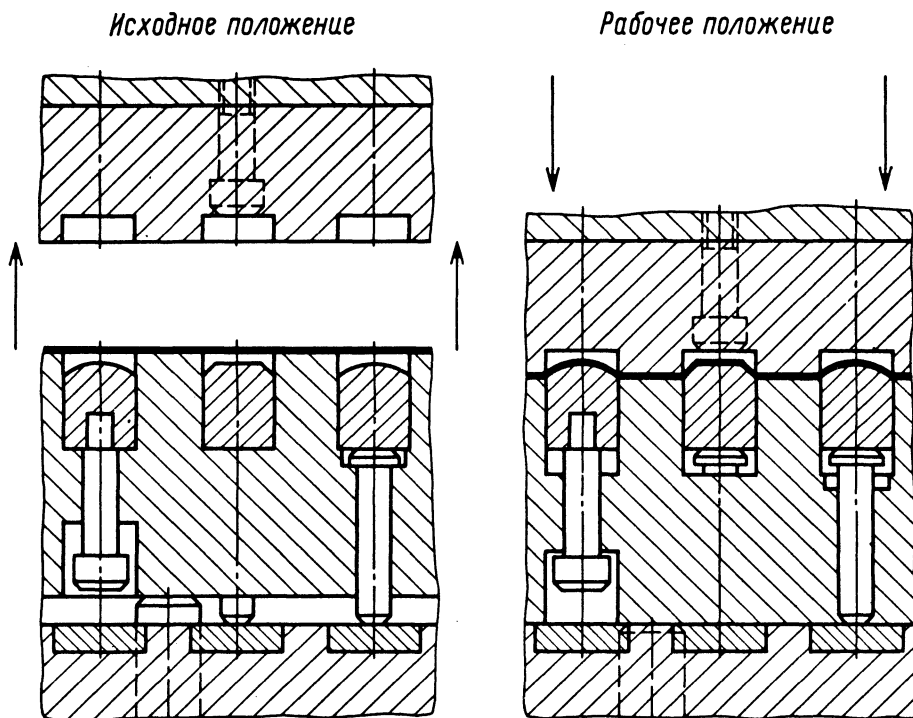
Рабочие части штампа для формовки ребер жесткости с применением складкодержателя
